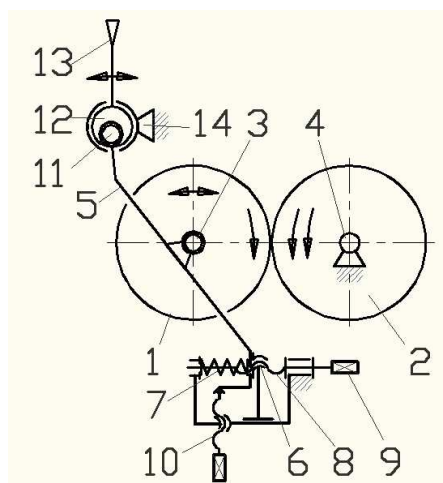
Схема установочного механизма с верхним расположением эксцентрикового вала
